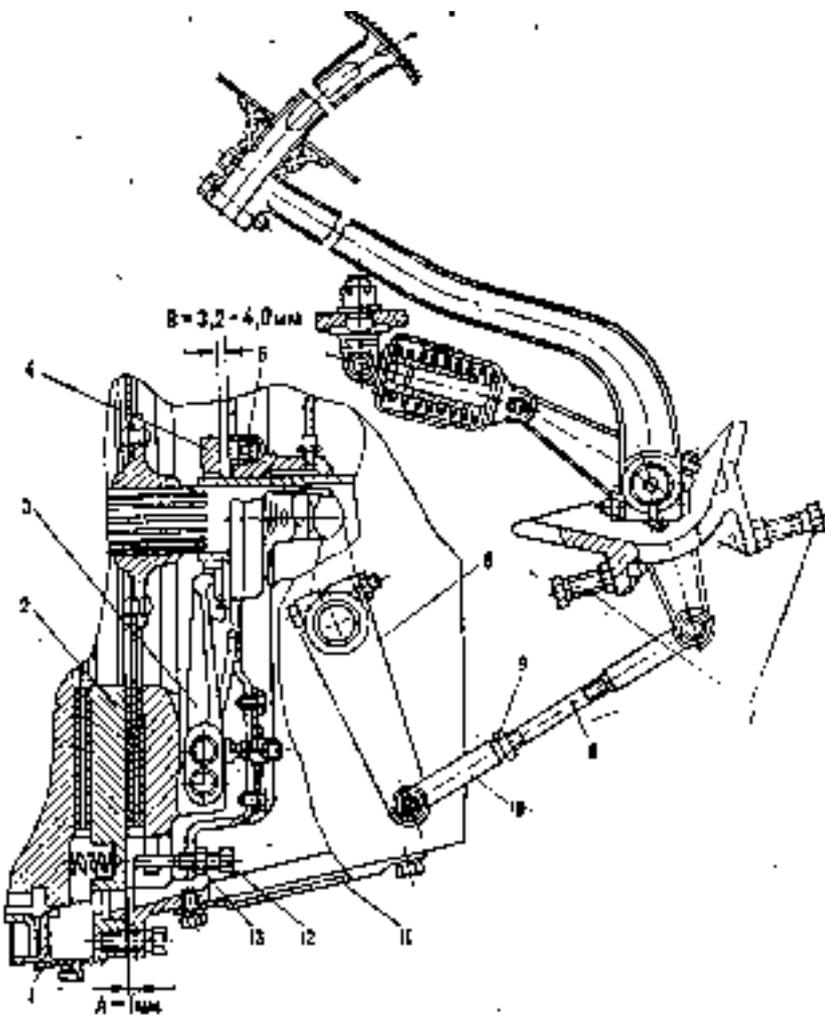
Регулировка сцепления автомобиля КраЗ-257
